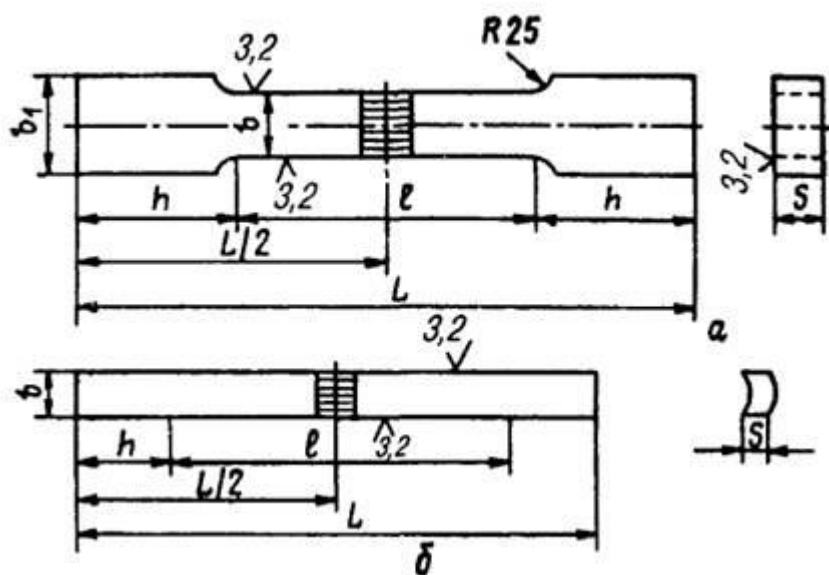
Форма и размеры образцов для испытаний сварных соединений на растяжение:
